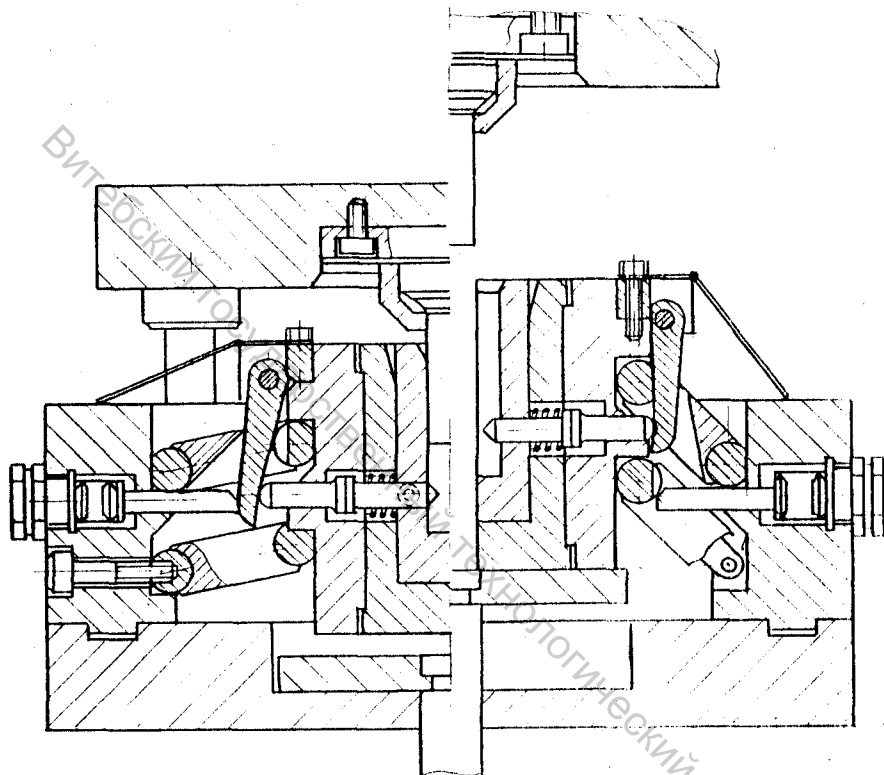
Типовой пакет рычажный с вертикальным разъемом матриц.
